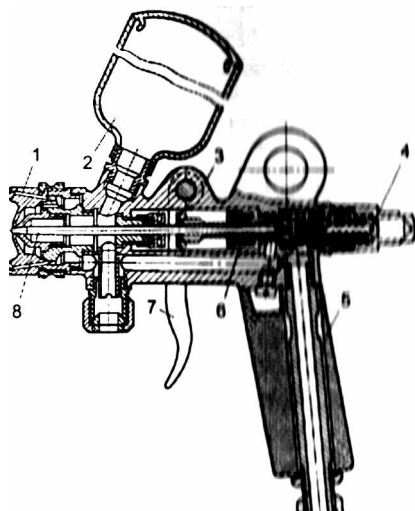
Пневматический распылитель лакокрасочных материалов: 1 — распылительная головка; 2 — бачок для краски; 3 — корпус распылителя; 4 — сопло; 5 — ручка; 6 — прокладка; 7 — спусковой крючок; 8 — наконечник иглы
